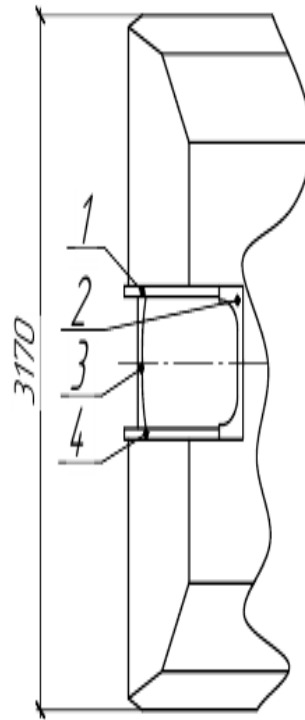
Вид зверху корпус спеціальної техніки типу «Ковпак»: 1 – права щока; 2 – верхня планка; 3 – нижня планка; 4 – ліва щока
